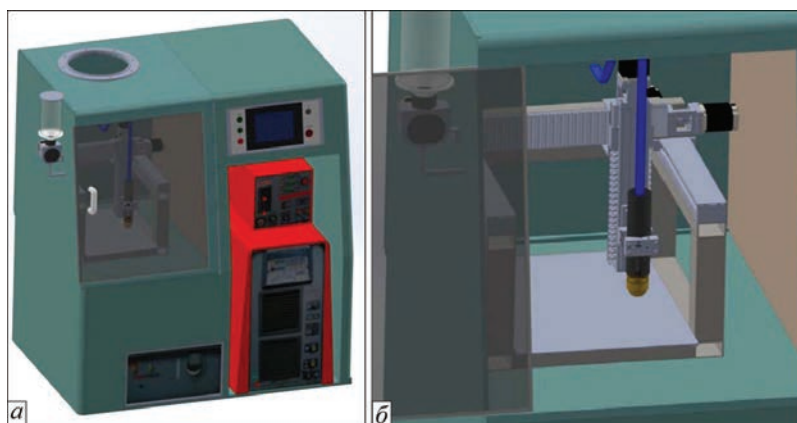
Спроектированный в ИЭС им. Е. О. Патона комплекс для изготовления трехмерных объектов на основе технологий плазменно-дуговой сварки и наплавки: а — общий вид; б — трехкоординатный манипулятор с плазмотроном
